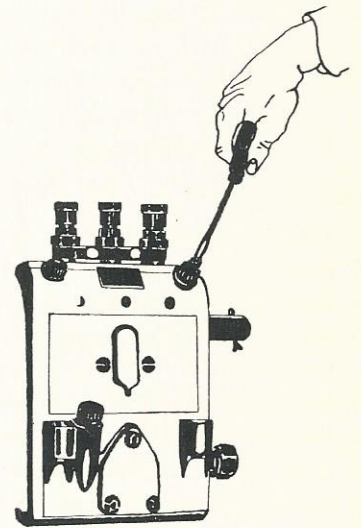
Entlüftung der Einspritzpumpe. Lösen der Entlüftungsschraube für Saugraum
